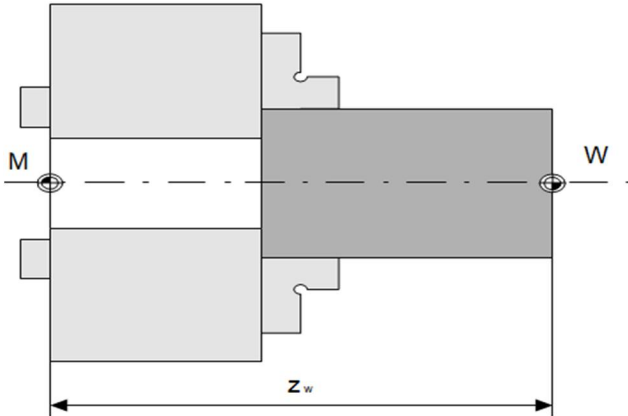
Встановлення нульової точки заготовки на токарному верстаті з ЧПК
